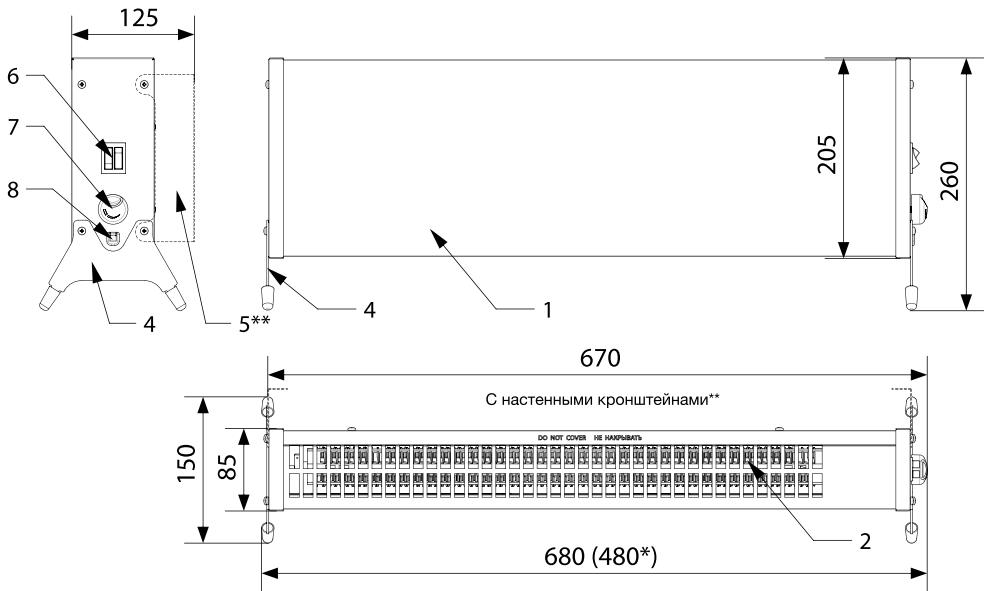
Габаритный чертеж и элементы конструкции электрического обогревателя.
